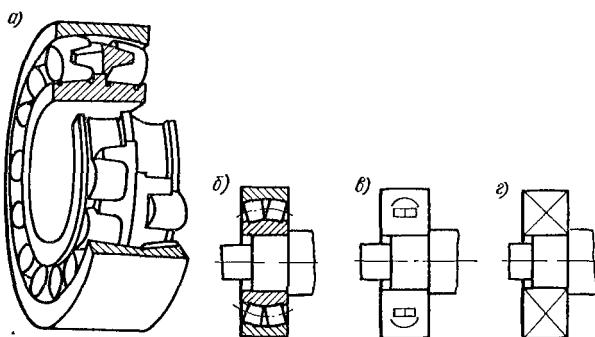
Радиальный роликовый двухрядный самонаводящийся сферический подшипник
